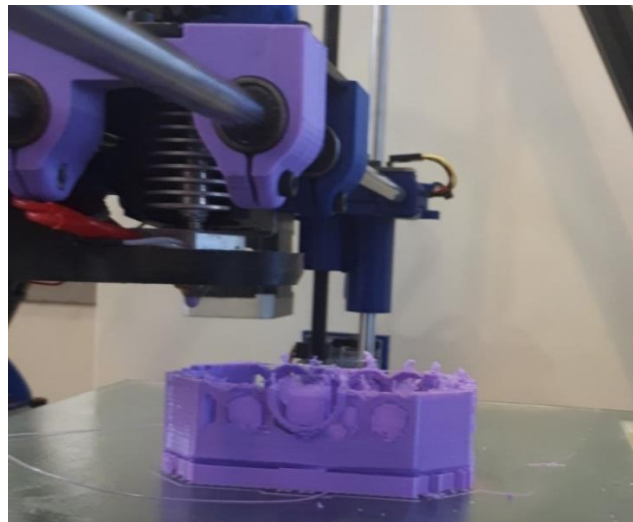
Cabezal en movimiento sin extrusión. Pieza en PLA color morado. Máquina 3D+.
